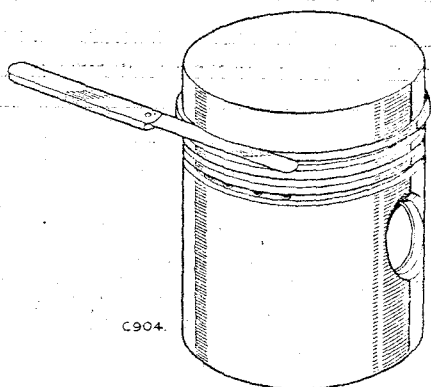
Comprobación de la tolerancia del aro en la ranura.
